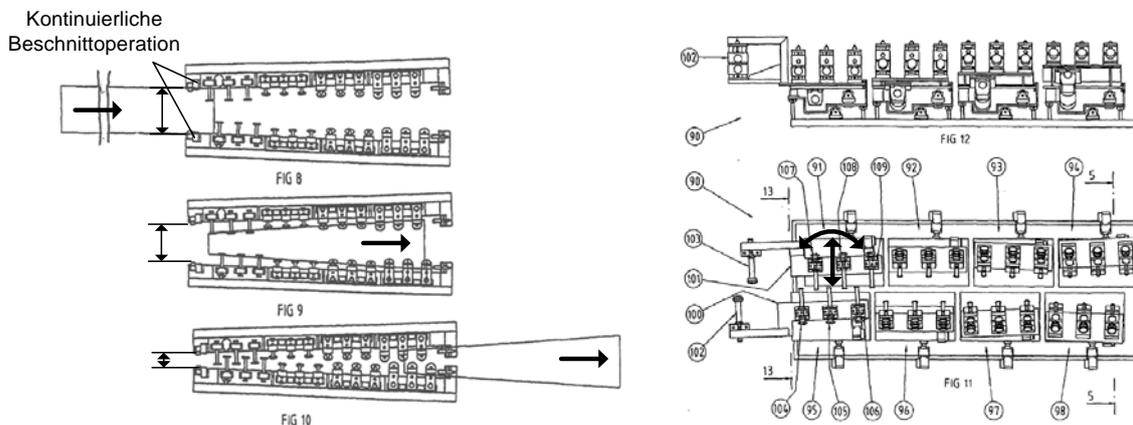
„Monroe-Verfahren“ mit kontinuierlichem Blechbeschnitt und beweglichen Gerüsthälften (links) oder flexibel positionierbaren Gerüstmodulen (rechts) nach INGVARSSON [32], [33]
